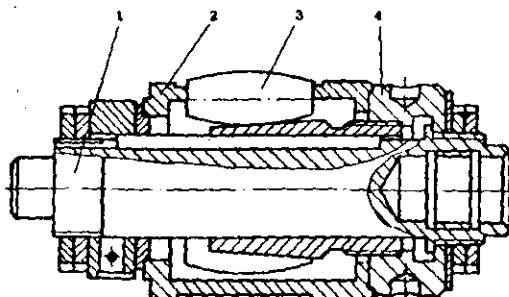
5. Роликовый раскатник для упрочнения зеркала цилиндра:
